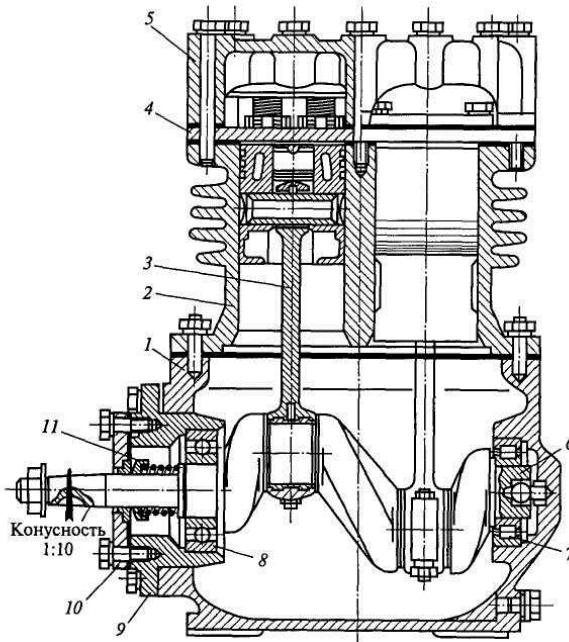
Відкритий непрямочинний фреоновий компресор ФВ6: 1 - картер; 2 - блок циліндрів; 3 - шатун з поршнем; 4 - клапанна дошка; 5 - кришка циліндрів; 6 – колінчастий вал; 7 - задній підшипник; 8 - передній підшипник; 9 - корпус підшипника; 10 - передня кришка; 11 - сальник
